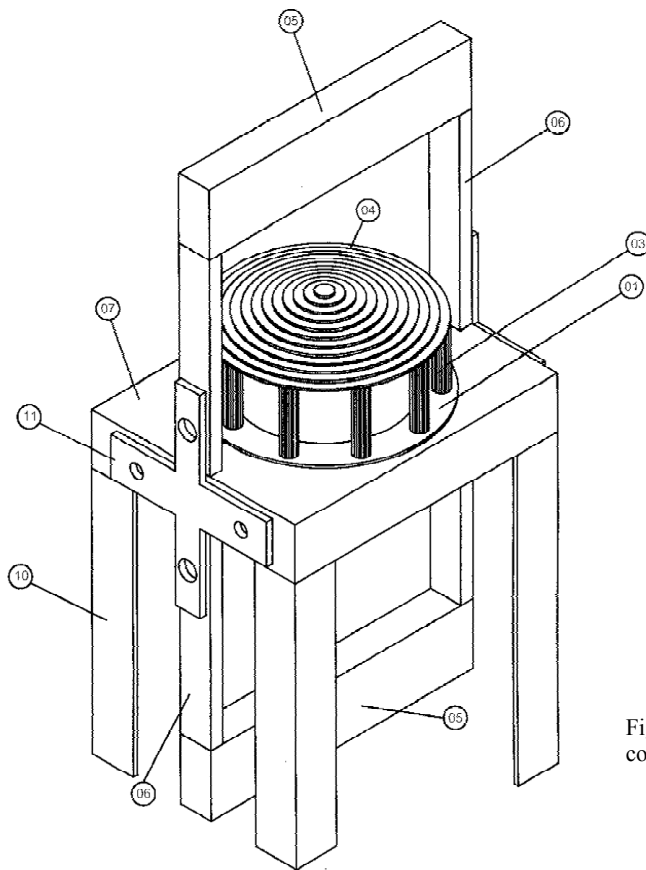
Desenho ilustrativo da máquina montada, sem conjunto hidráulico.
